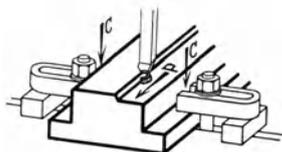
Aufnahme der Schnittkraft beim Spannen. P Schnittdruck, C Spanndruck.
